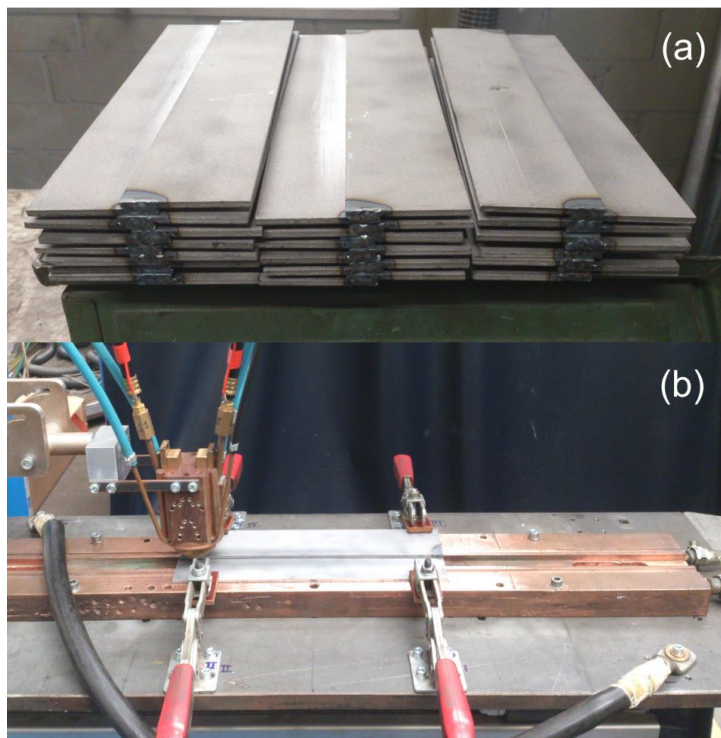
Imagens mostrando os corpos de prova para ensaio de soldagem em junta sobreposta. (a) corpos de prova ponteados. (b) corpos de prova fixados na mesa de soldagem
